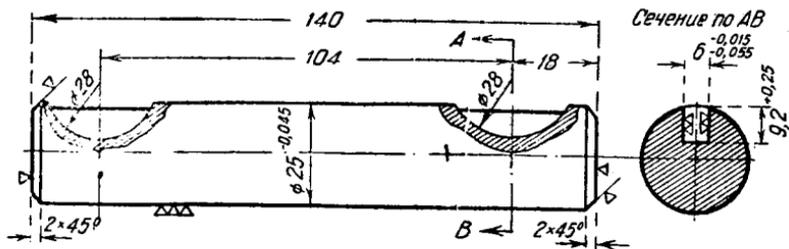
Дет. 18-32. Длинный валик вилки муфты сцепления
